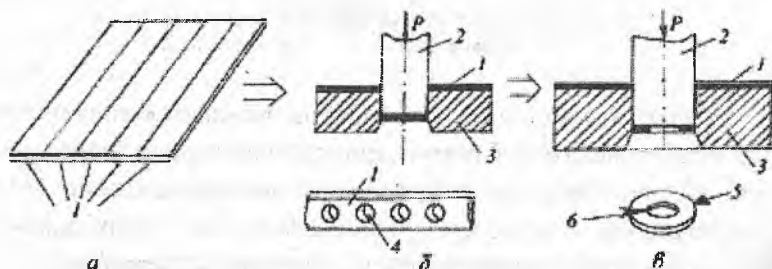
Схема процесса изготовления шайбы: а - отрезка; б - пробивка отверстия; в - вырубка шайбы; 1 - полоса, 2 - пуансон, 3 - матрица, 4 - отверстие, 5 - пробивка, 6 - вырубка
